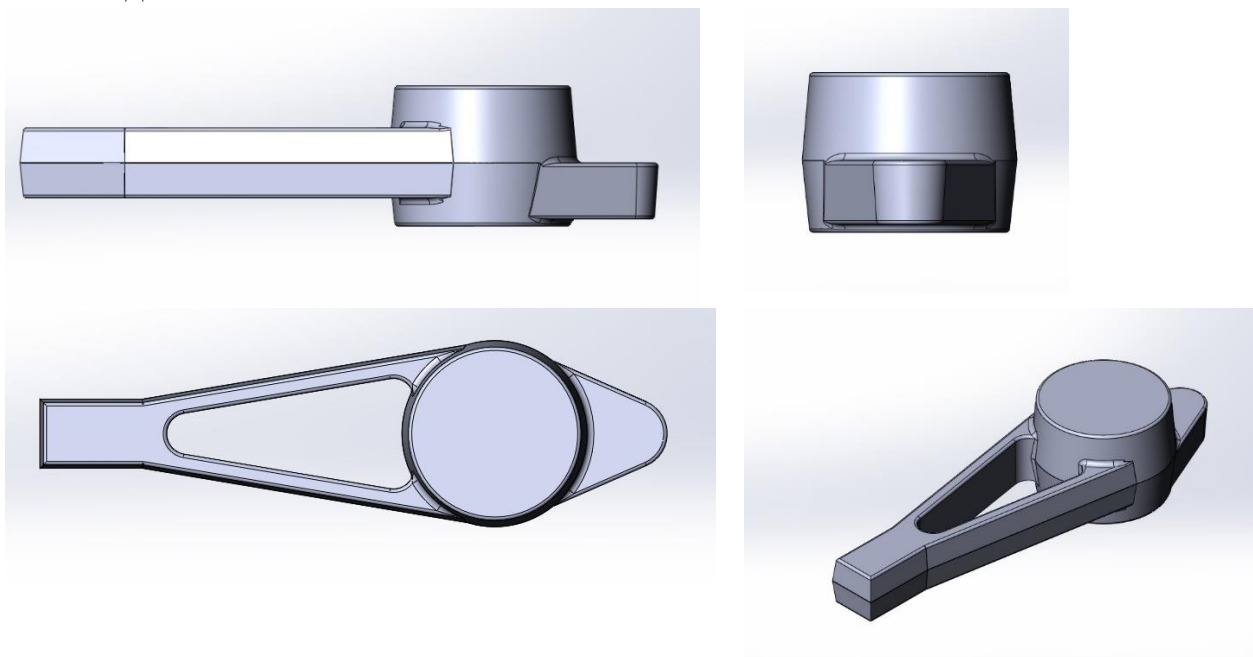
Комп'ютерна 3D-модель заготовки деталі «Качалка»
